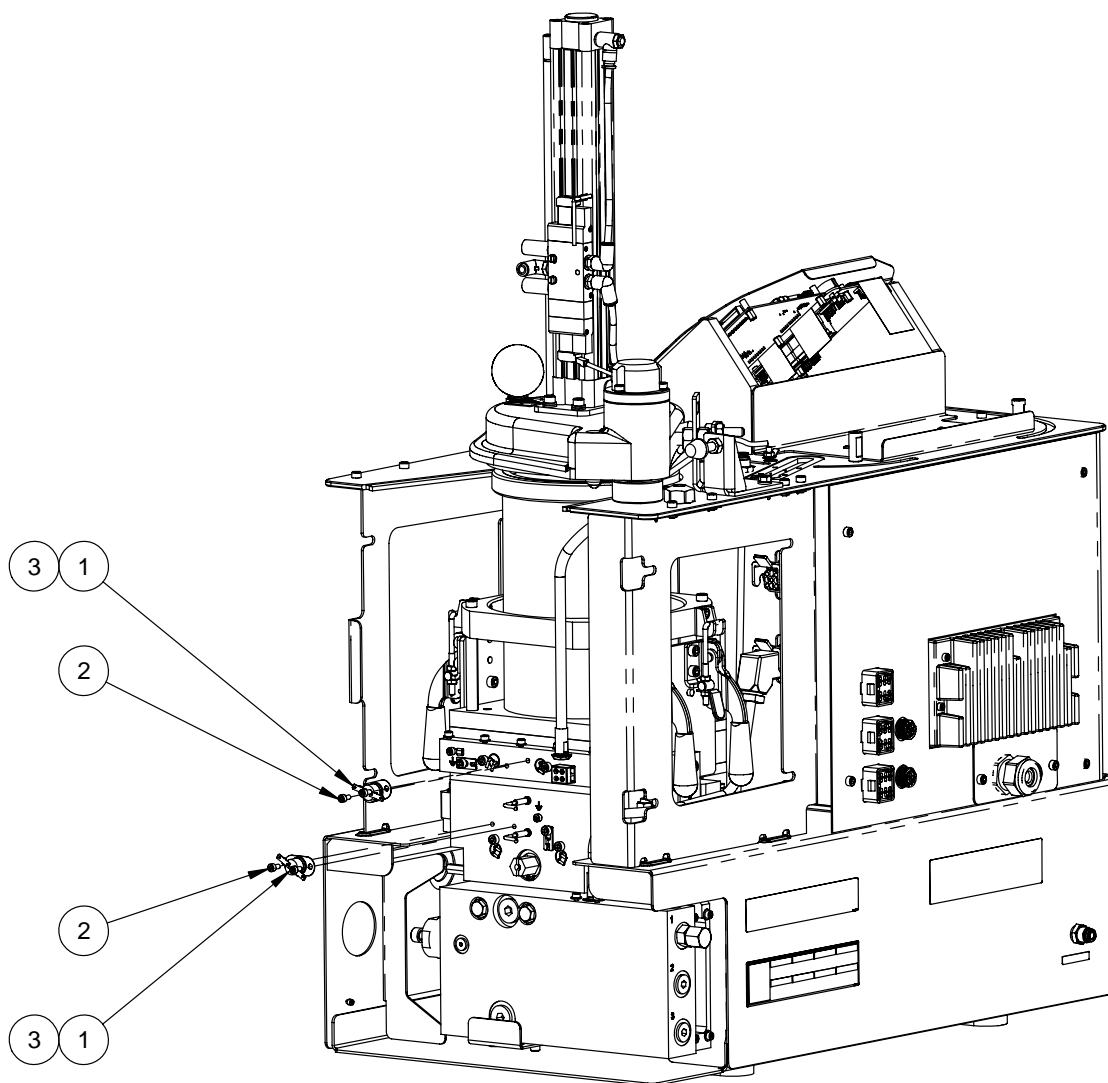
Ersatzteile Baugruppe Thermostat
